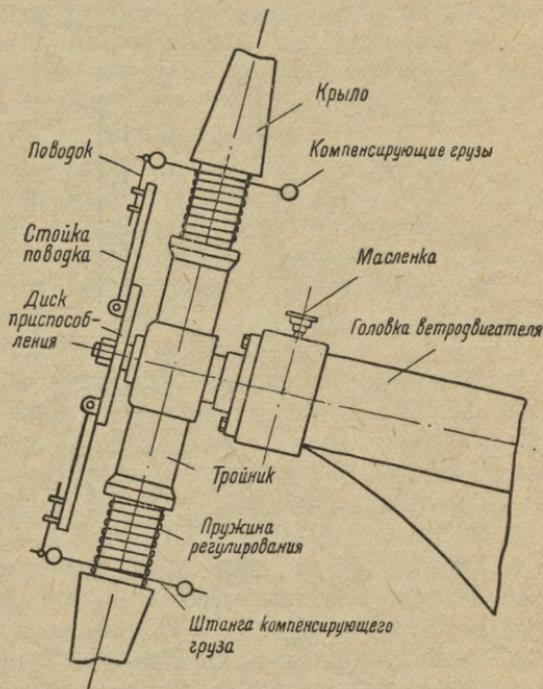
Приспособление к механизму регулирования т. Беднякова (вид сбоку)
